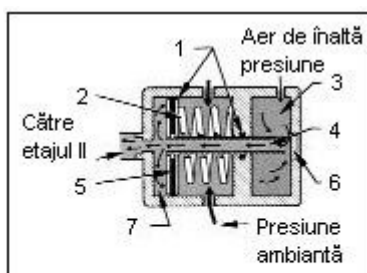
Etaj I de tip echilibrat, cu piston clapet. 1-O-ring-uri; 2-arc tarat; 3-cameră de înaltă presiune;
